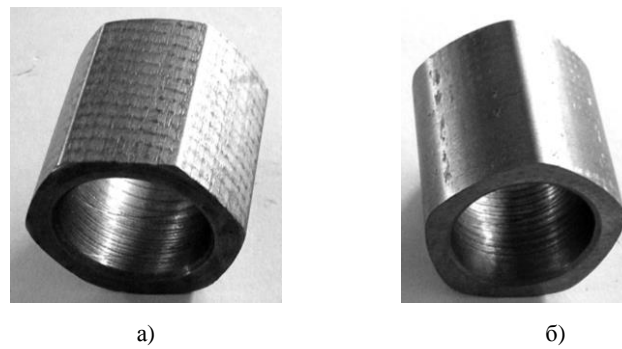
Образцы, обработанные эксцентрично установленной цилиндрической фрезой (а); опилованием (б)
